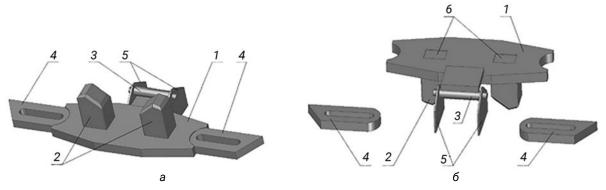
Плита с двумя упорами 31883-НСБ: a- рабочее положение; 6- нерабочее положение; 1- плита опорная; 2- упоры; 3- ось; 4- плита фиксирующая; 5- кронштейны; 6- место сварки
